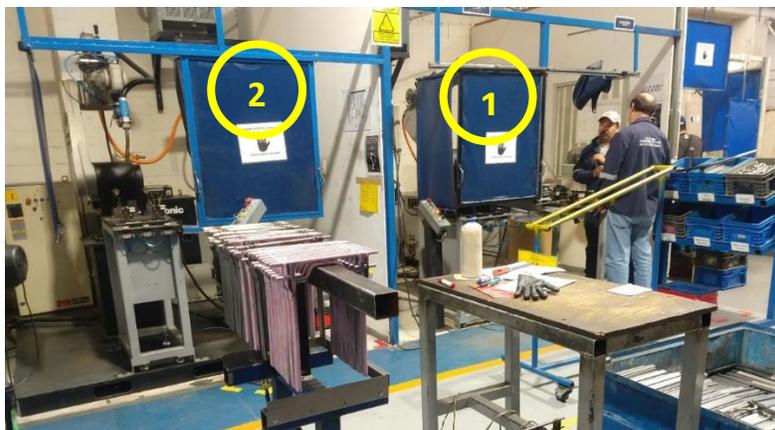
Estaciones de soldadura para MAL HINTEN
